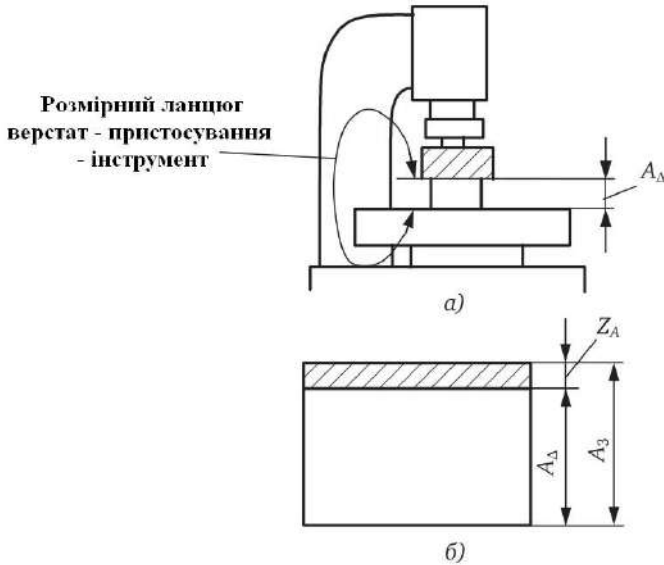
Технологічний розмірний ланцюг розміру деталі та системи «верстат – пристосування – інструмент»
